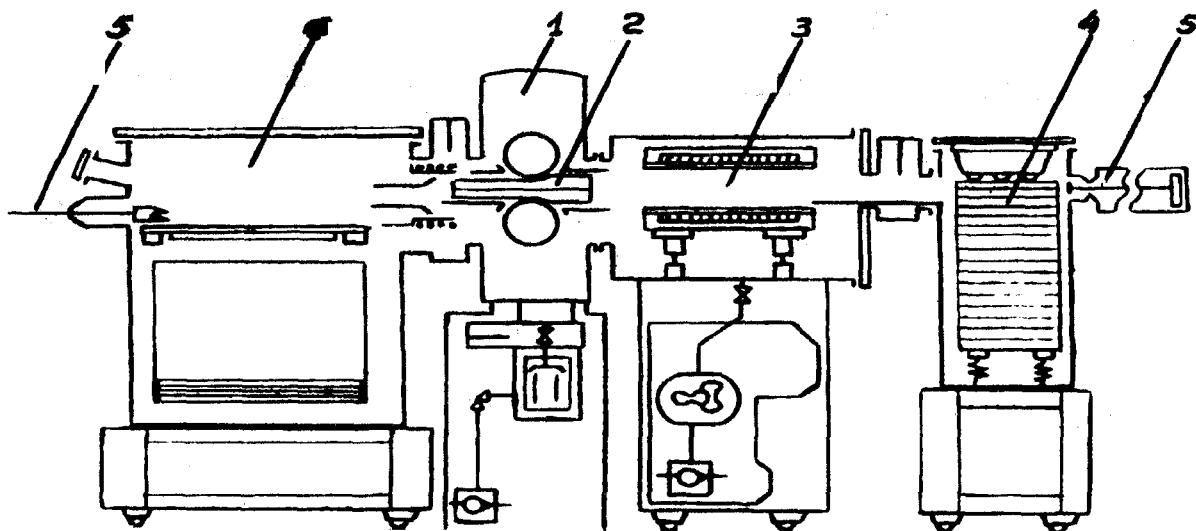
Схема вакуумного прокатного стана СВАПР-1; 1 - клеть стана; 2 - прокатываемая заготовка; 3 - печь нагрева заготовки; 4 - камера загрузки; 5 - манипуляторы; 6 - камера выгрузки.
